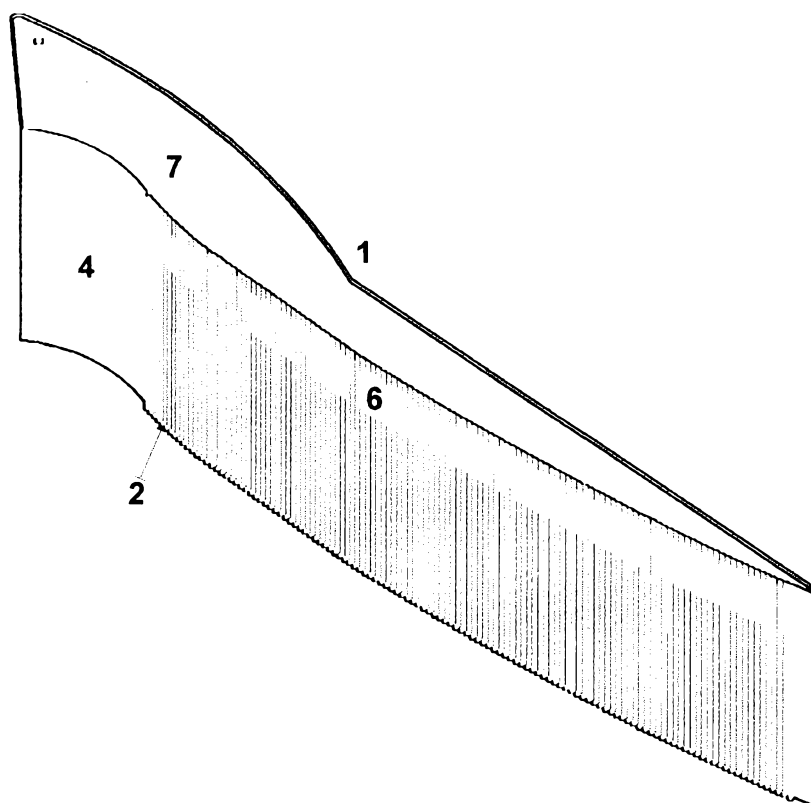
Gezoomte Teilansicht 3D aus Fig. 6 des Spaltsiebes (6) und der Einlaufstrecke (4)
